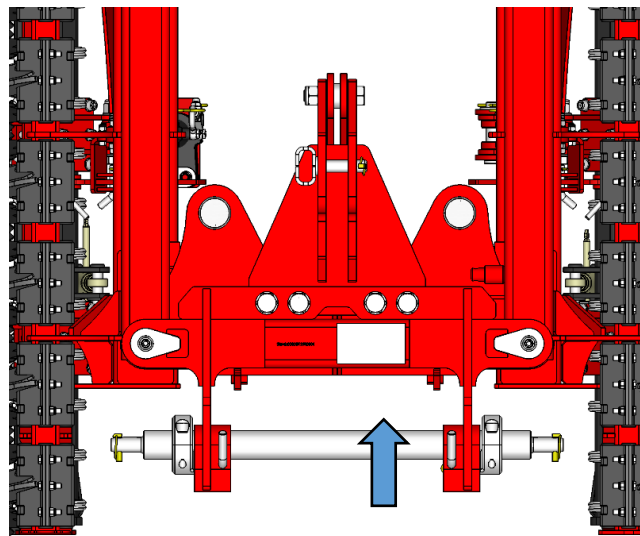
tabEmplacement de la plaque signalétique et du numéro VIN du véhicule sur la machine
